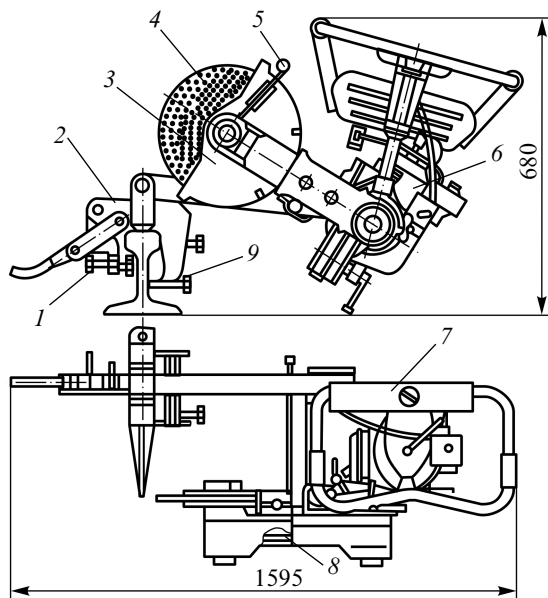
Рельсореальный абразивно-отрезной станок РМК:
